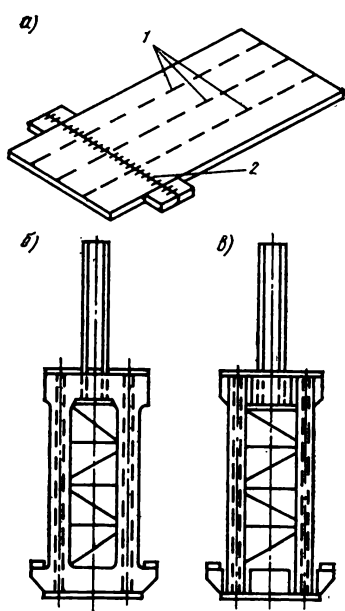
Примеры конструктивных решений, позволяющих расширить область применения автоматической сварки
